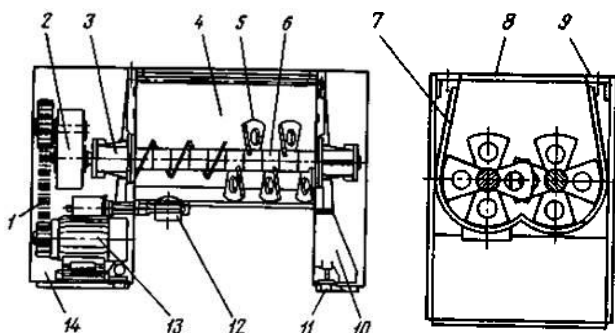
Двухроторный лопастной смеситель: 1 – ременная передача; 2 – редуктор; 3 – опоры; 4 – корпус; 5 – фигурные лопасти; 6 – горизонтальные валы; 7 – рубашка; 8 – решетки; 9 – крышка; 10 – станина; 11 – месдозы; 12 – разгрузочный патрубок; 13 – электродвигатель; 14 – ограждения
